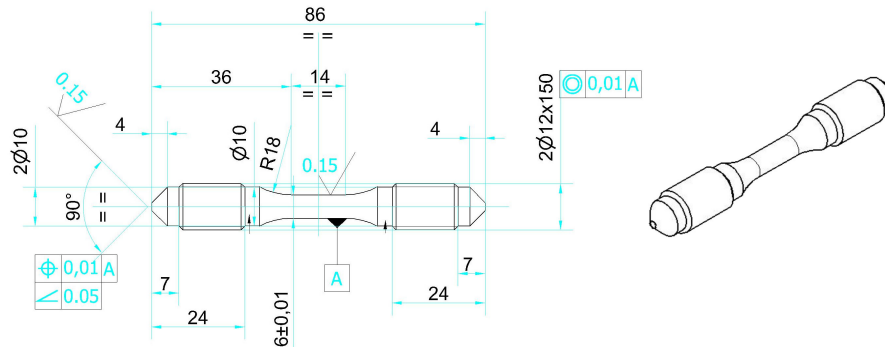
Géométrie d'éprouvette de fatigue.
